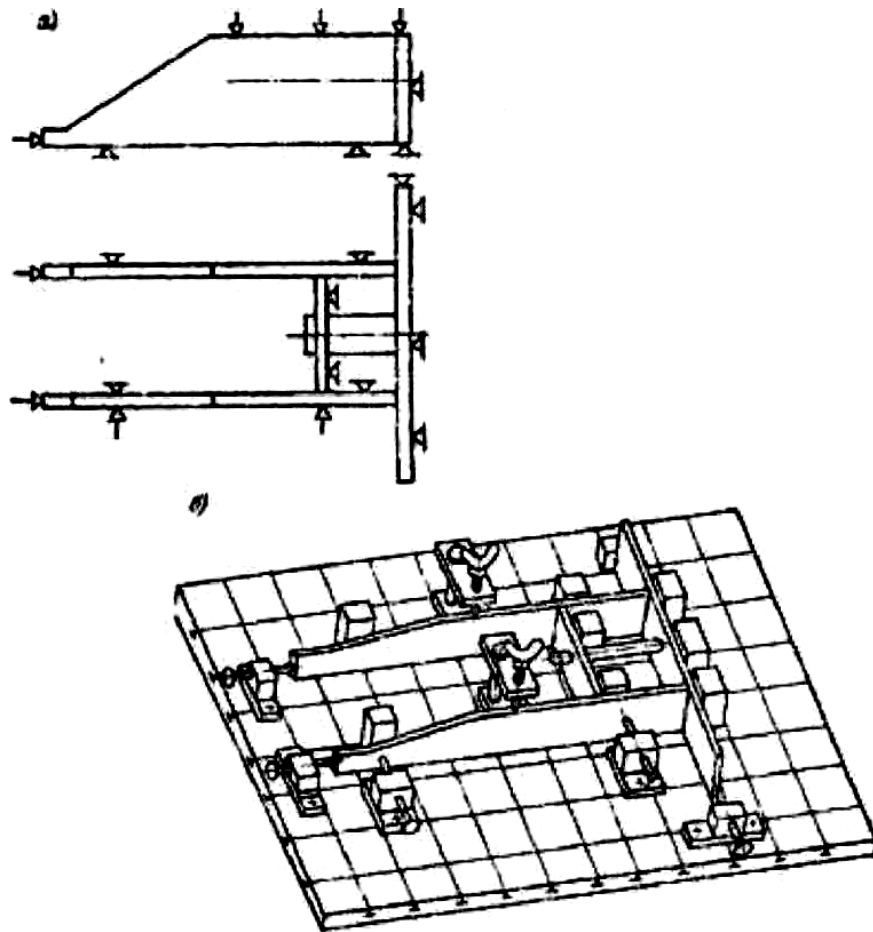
Принципиальная схема приспособления для сборки и сварки кронштейна (а) и общий вид УСПС (б)
